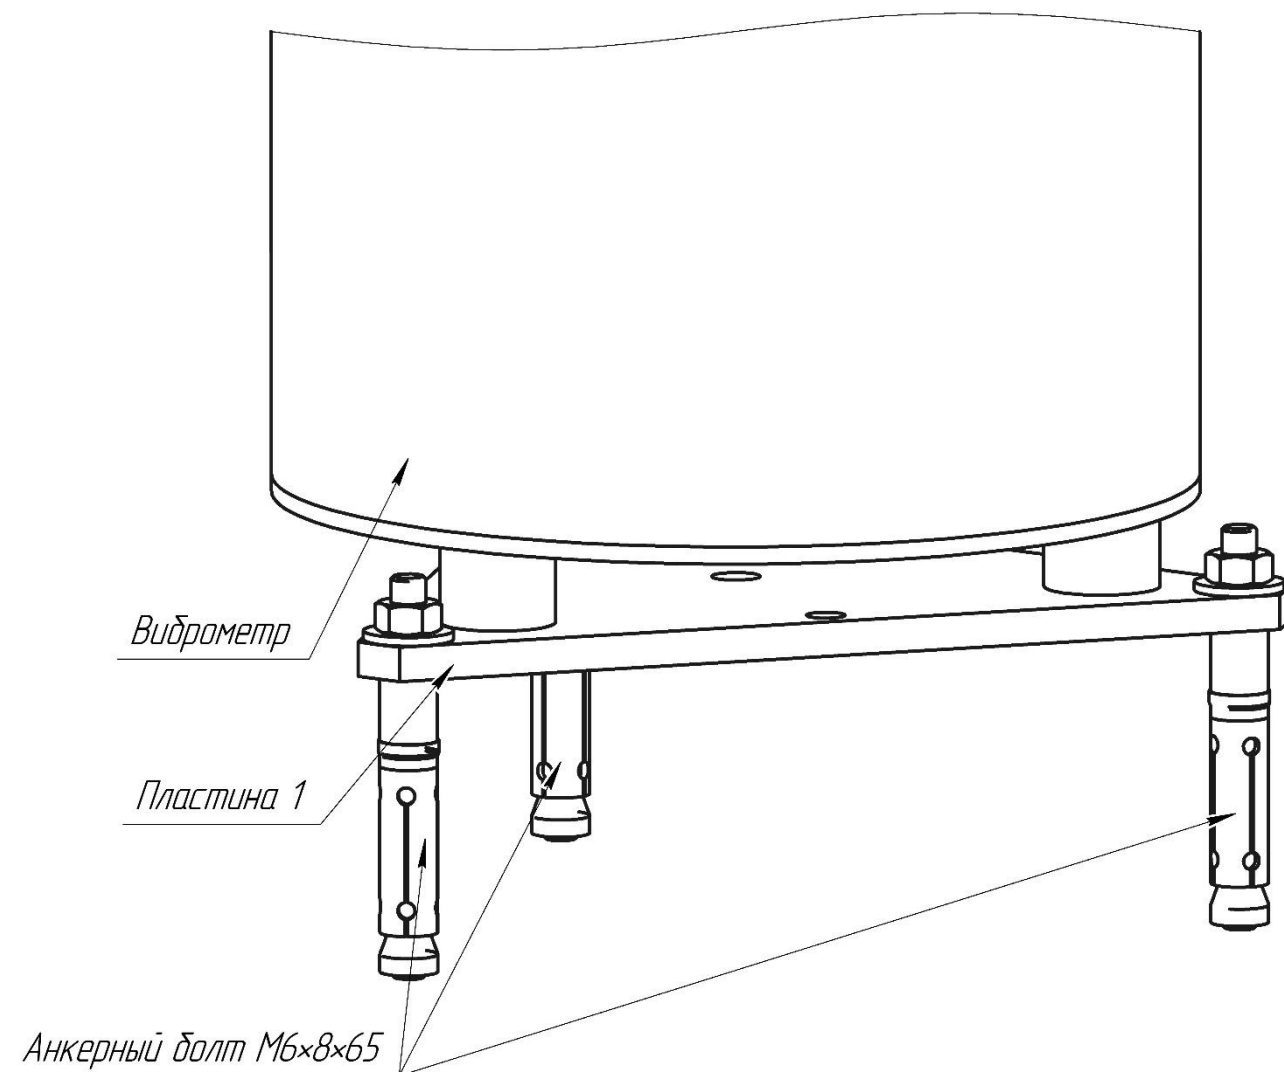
Крепление виброметра без регулировки – Шаг 2
